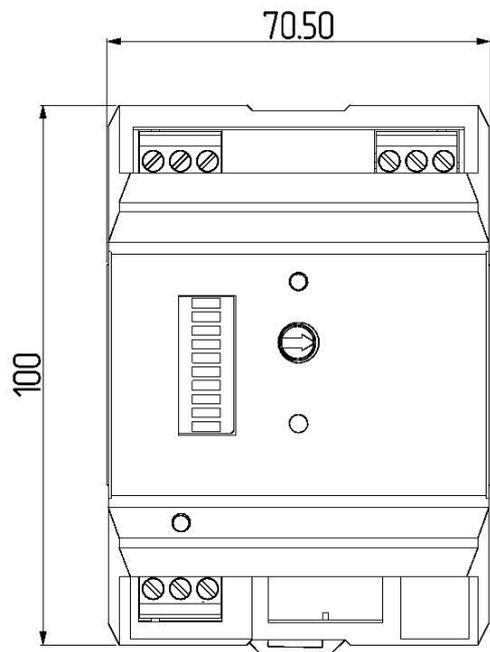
Внешний вид. Габаритный чертёж РКСИ-1002
